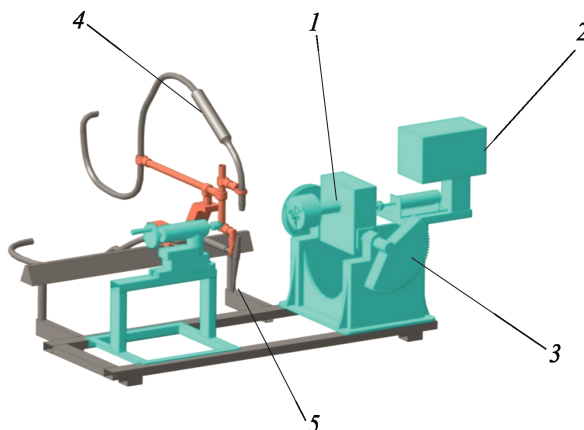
Схема лабораторной установки: 1 – патрон; 2 – двигатель; 3 – редуктор; 4 – горелка; 5 – горелка для сопутствующего подогрева
